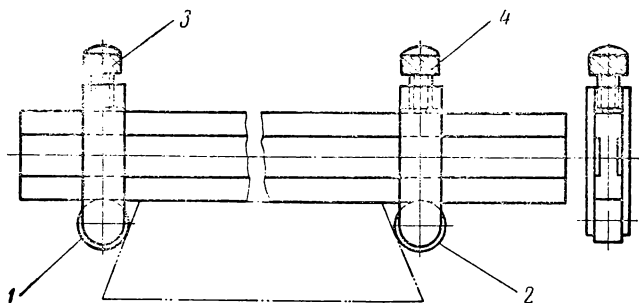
Роликовое приспособление для проверки конических поверхностей
